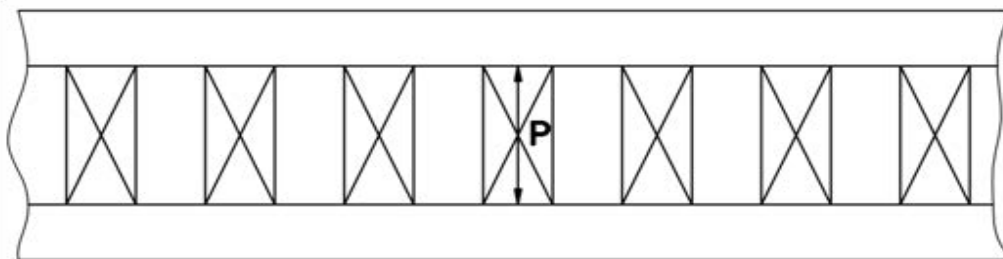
Схема разжима полок сварной станины суппортов станка
